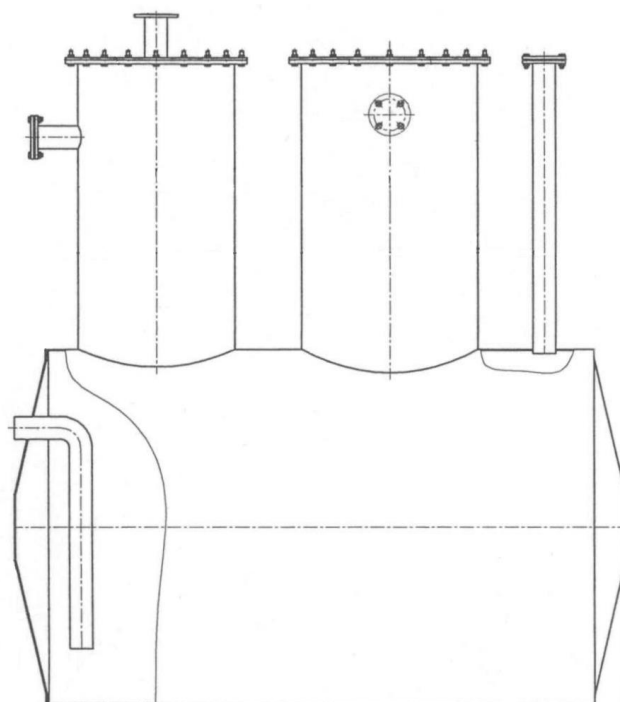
Общий вид эскиза резервуаров РГС-5
